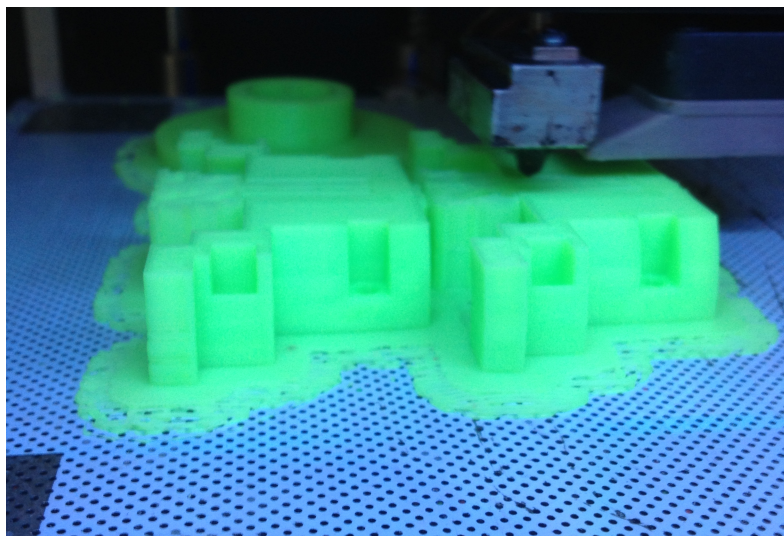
Fabricación del Molde. Durante el proceso de fabricación de los moldes. (Fuente: Propia)
